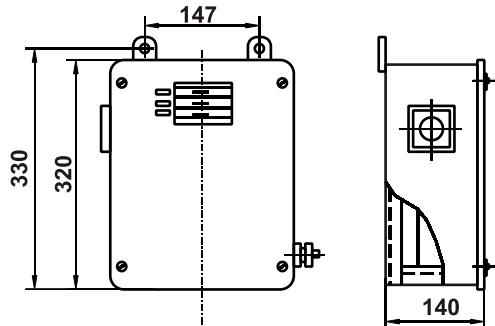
Внешний вид и габаритные размеры ЯТП-0,25
